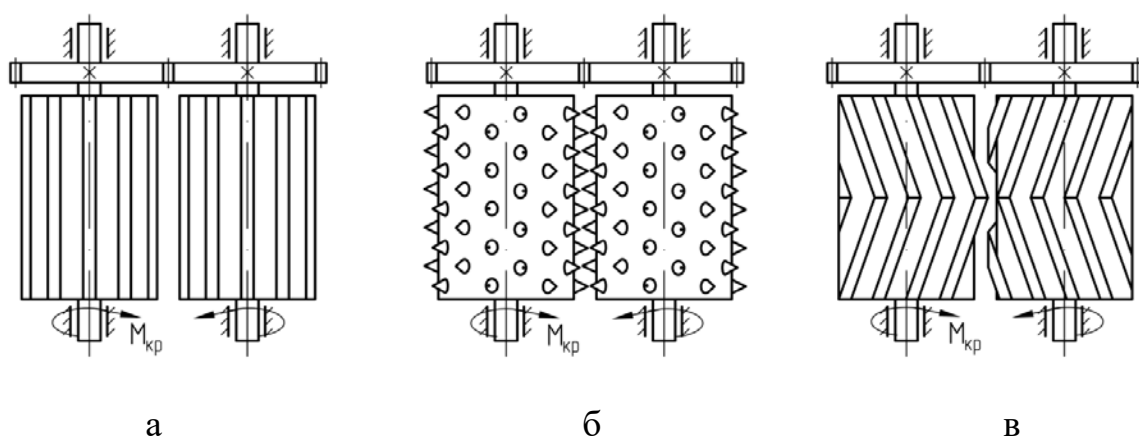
Пресс-валковые уплотнители с развитой рабочей поверхностью валков:
